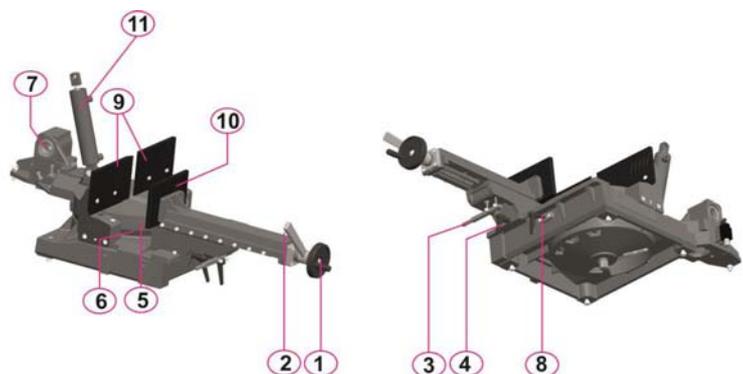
Maschinenteile Schraubstock und Drehtisch
